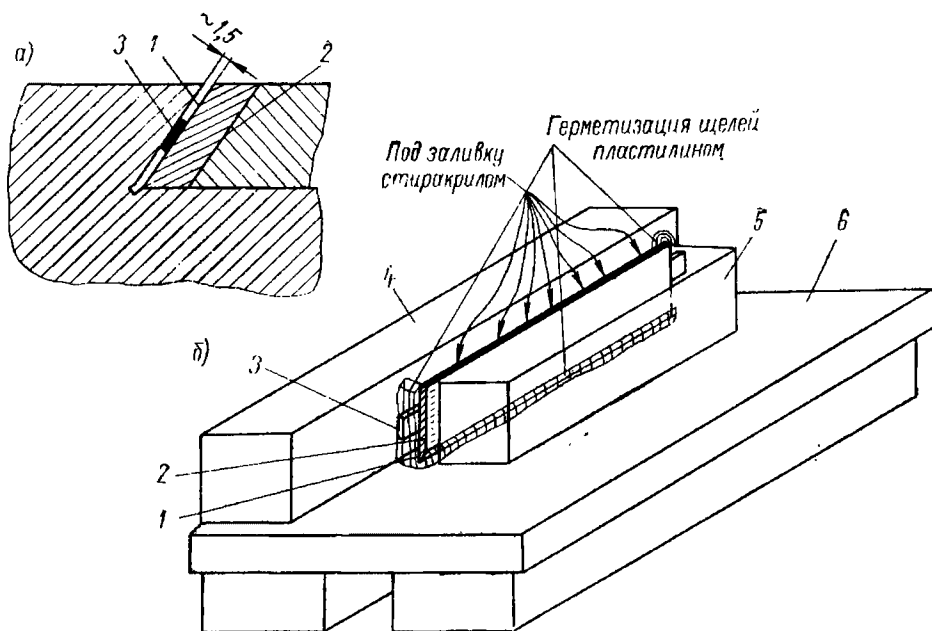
Восстановление клиньев: а — замер щели мерными плитками; б — установка клина для наращивания поверхности
